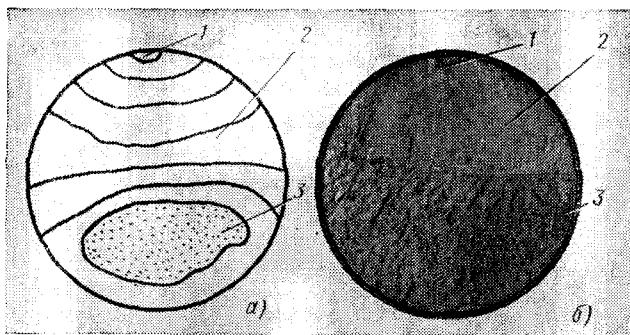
Излом при усталостном разрушении: а — схема излома; б — макроструктура излома; 1 — очаг зарождения трещины; 2 — излом; 3 — зона долома
